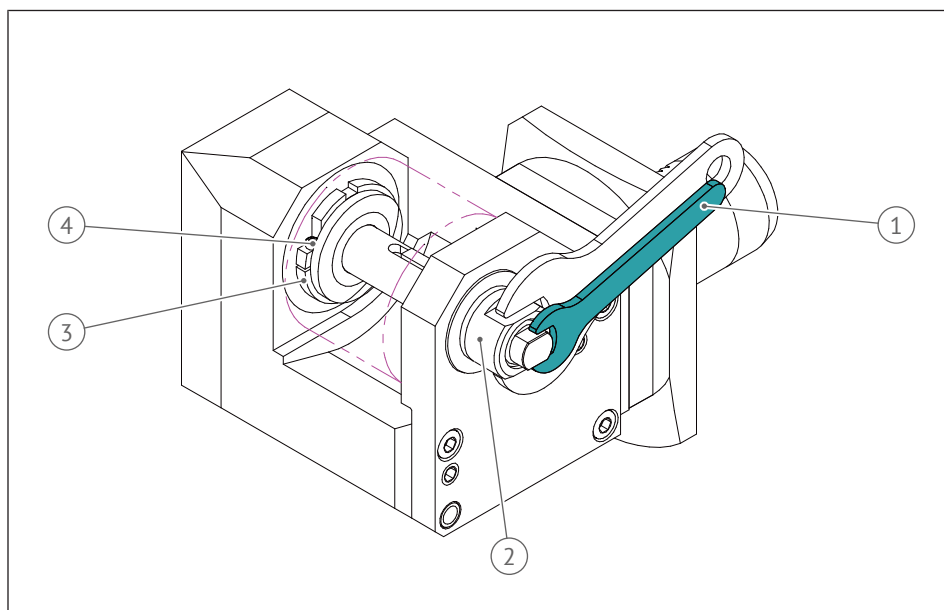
Einstellen des Fräserpakets am Scheibenfräserkopf
